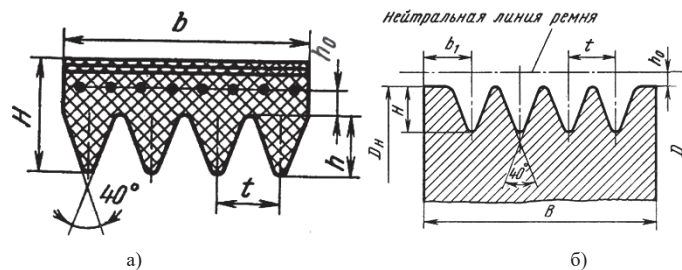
Сечение поликлинового: а – ремня; б – шкива
